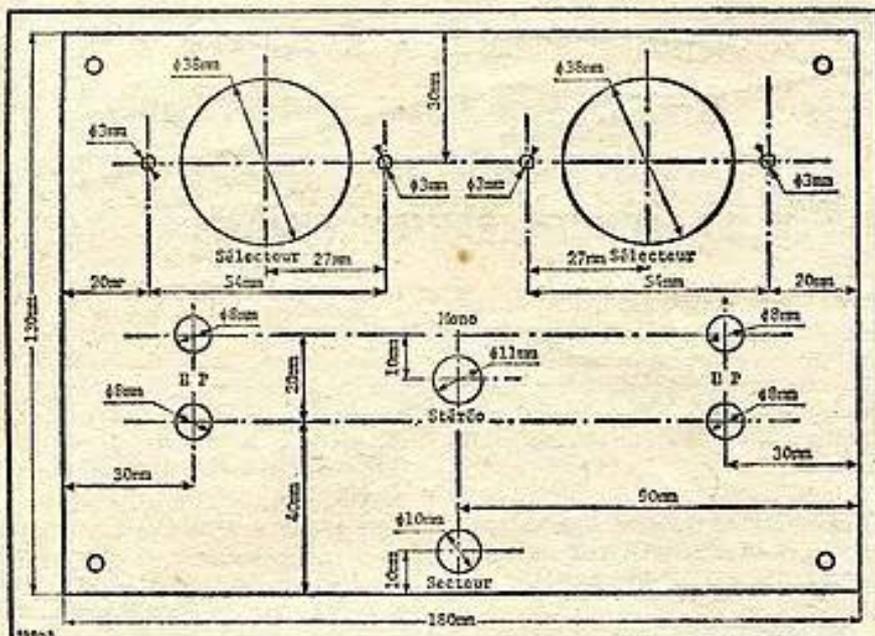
Dimensions et cotes de perçage de la plaque avant. — N.B. la plaque peut être en une ou deux parties.
